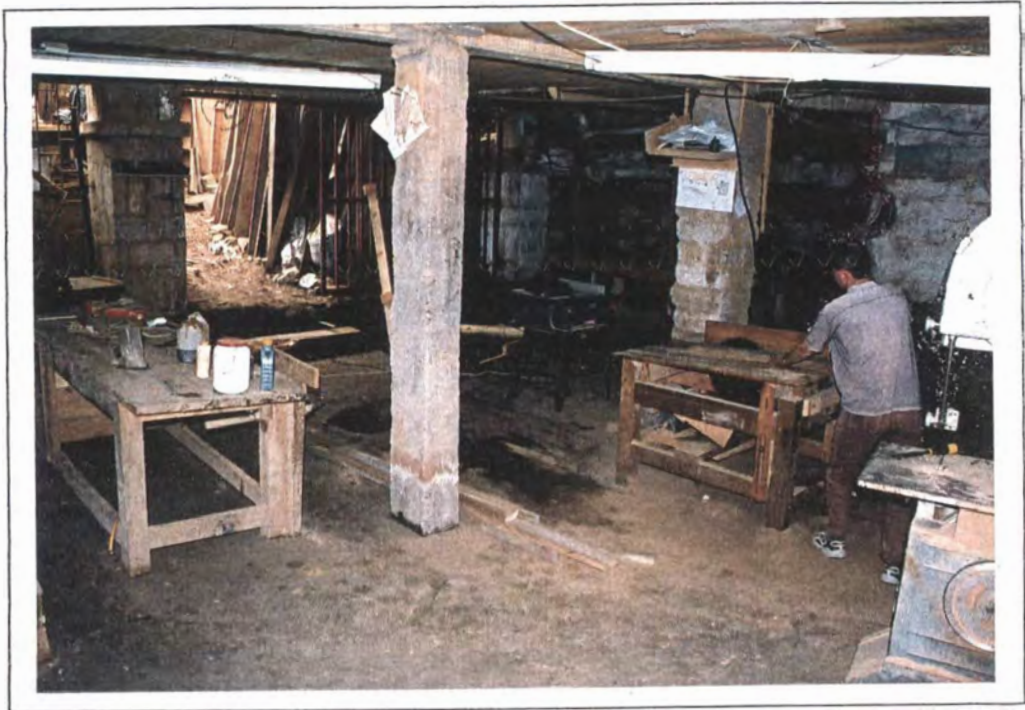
TALLER DE MAQUINAS / MADEROS DE LA FE
